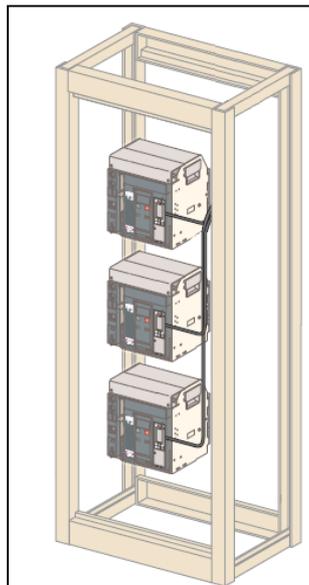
MODULO DE ACCIONAMIENTO.
